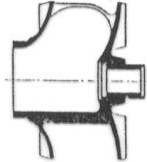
Geschlossenes Einschufelrad (Draufsicht ohne
